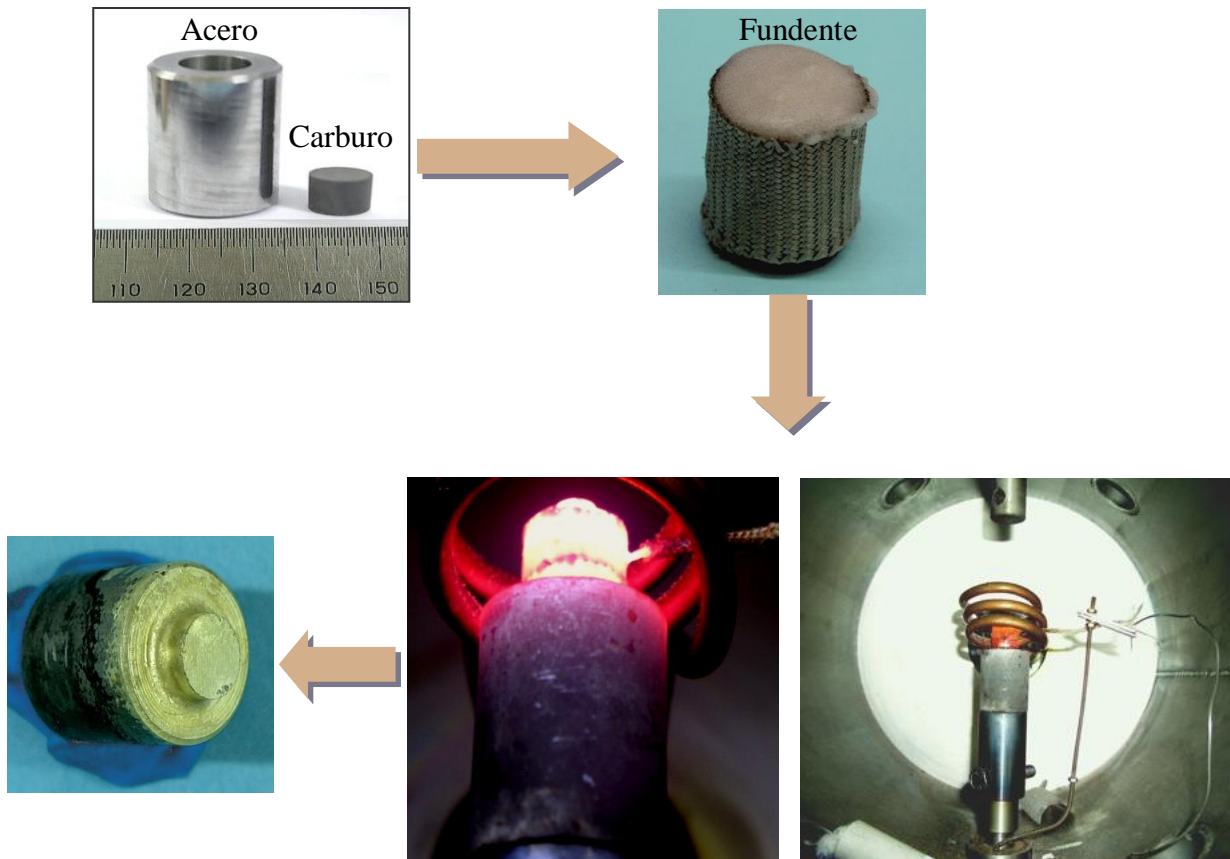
Imágenes del proceso de soldadura en Horno de Inducción.
